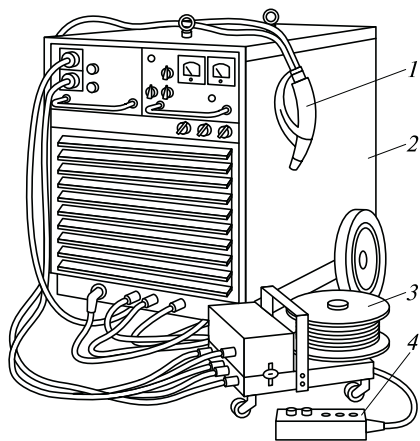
Сварочный полуавтомат ПДГ-502:
